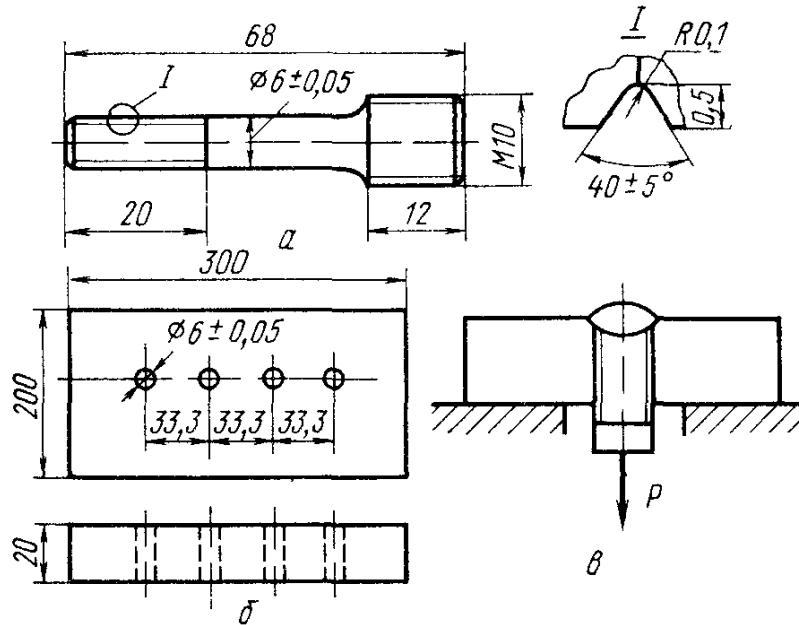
Образец вставка (а), пластина под сварку (б) и схема нагружения образца (в) по методу «Имплант»
